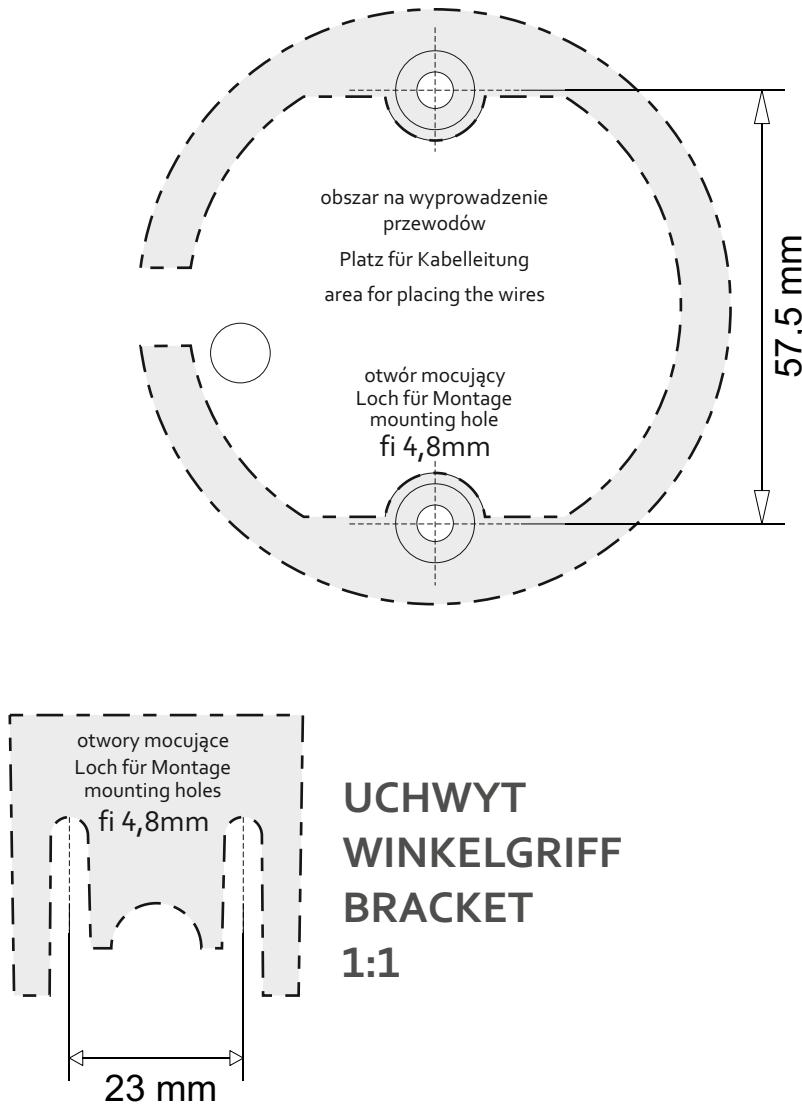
Montaż lampy do powierzchni pionowej za pośrednictwem uchwytu kątowego.
